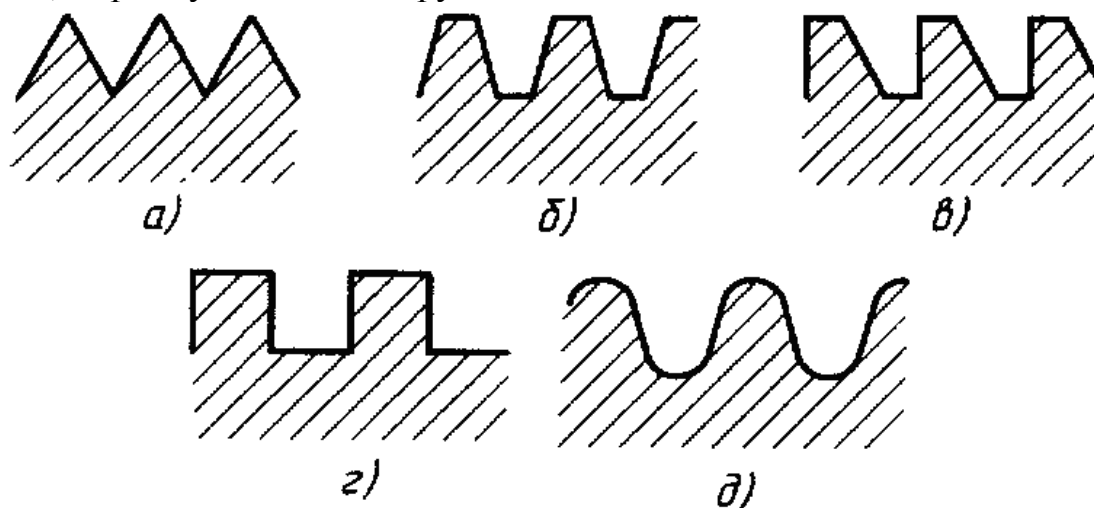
Форма профиля резьбы (а-треугольный; б-трапецеидальный; в-упорный; г-прямоугольный; д-круглый)
